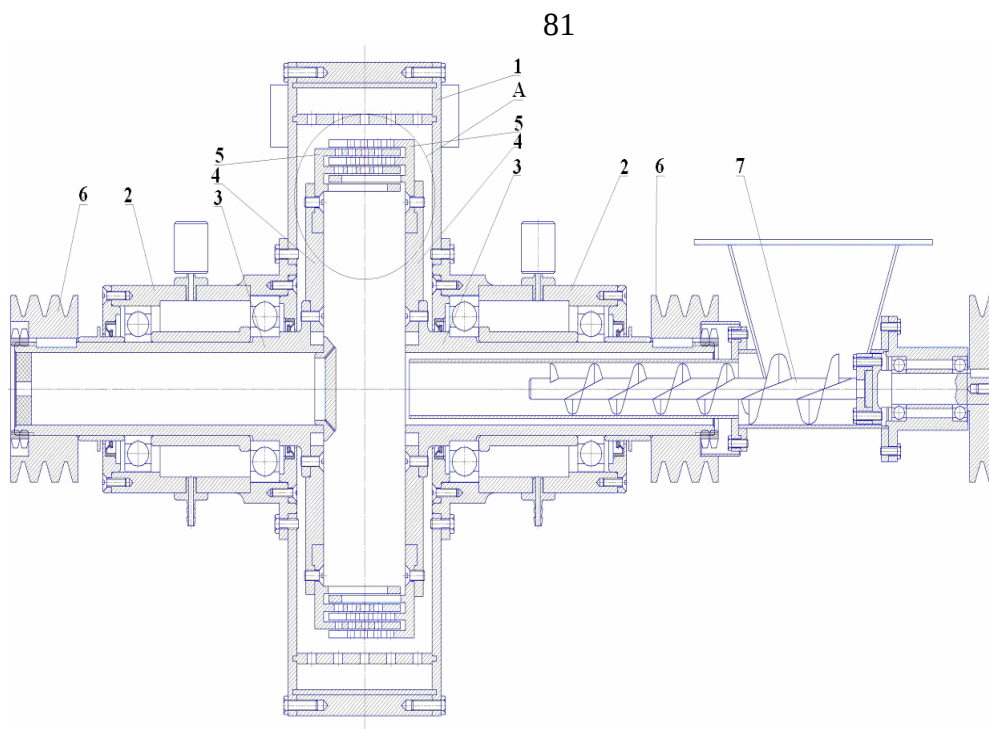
Вид общий дезинтегратора: 1 – помольная камера; 2 – корпус шпинделя; 3 – опора; 4 – диск ротора; 5 – рабочие кольца; 6 – шкив; 7 – загрузочный шнек.
